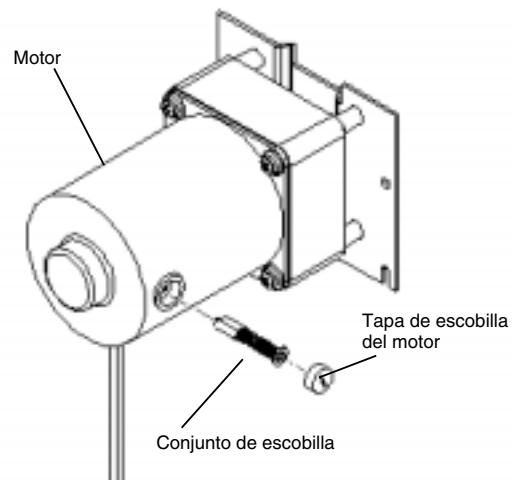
PARA CAMBIAR LA ESCOBILLA DEL MOTOR
